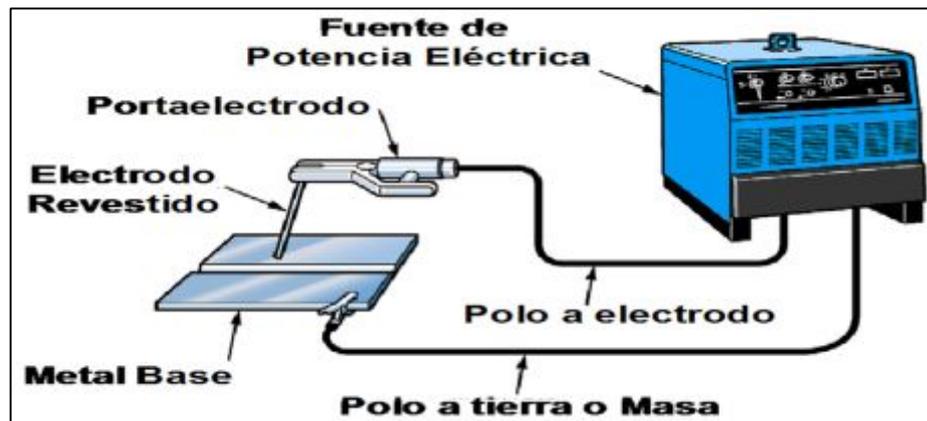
Circuito Soldadura Arco Eléctrico
